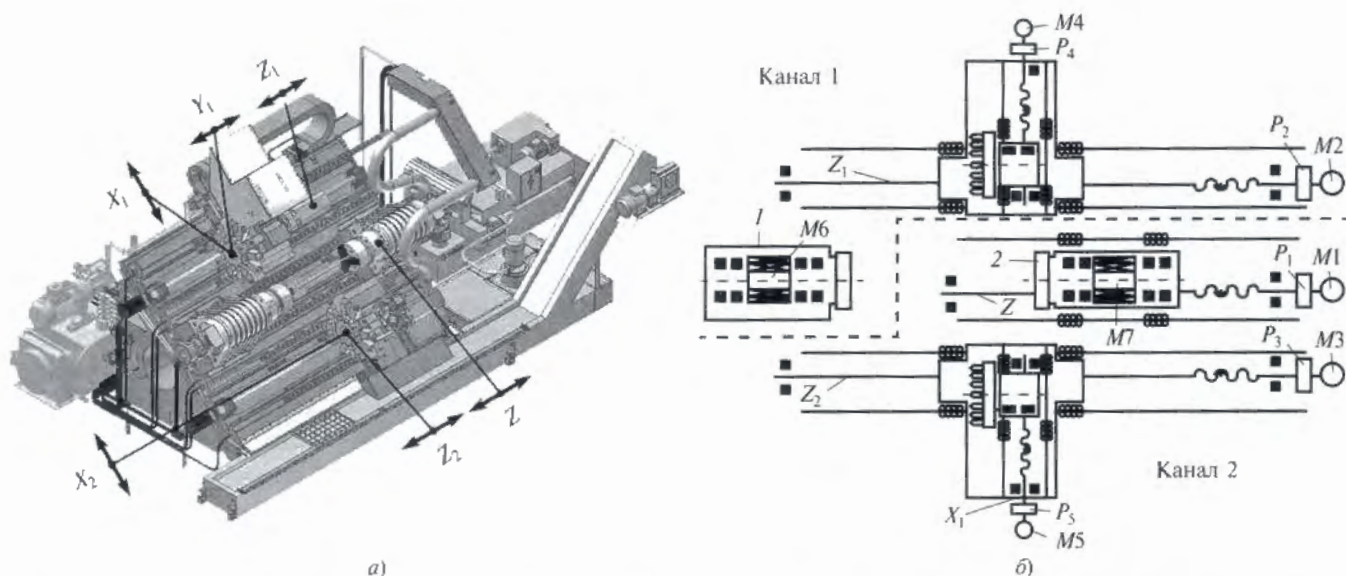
Токарно-фрезерный ОЦ мод. «НАКЛОН 535» наклонной компоновки: а — общий вид; б — кинематическая схема (1 — главный привод; 2 — противопиндель)
